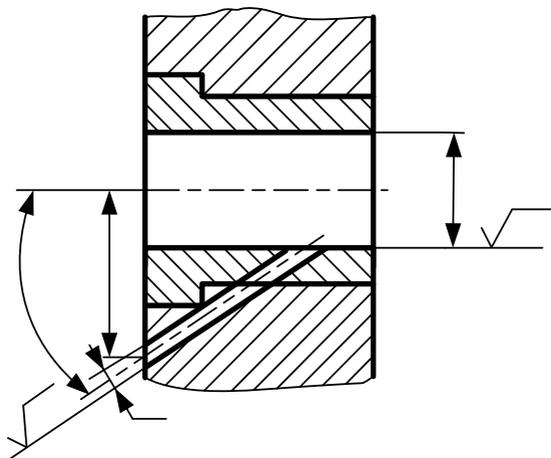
Обозначения при обработке в процессе сборки на сборочном чертеже
